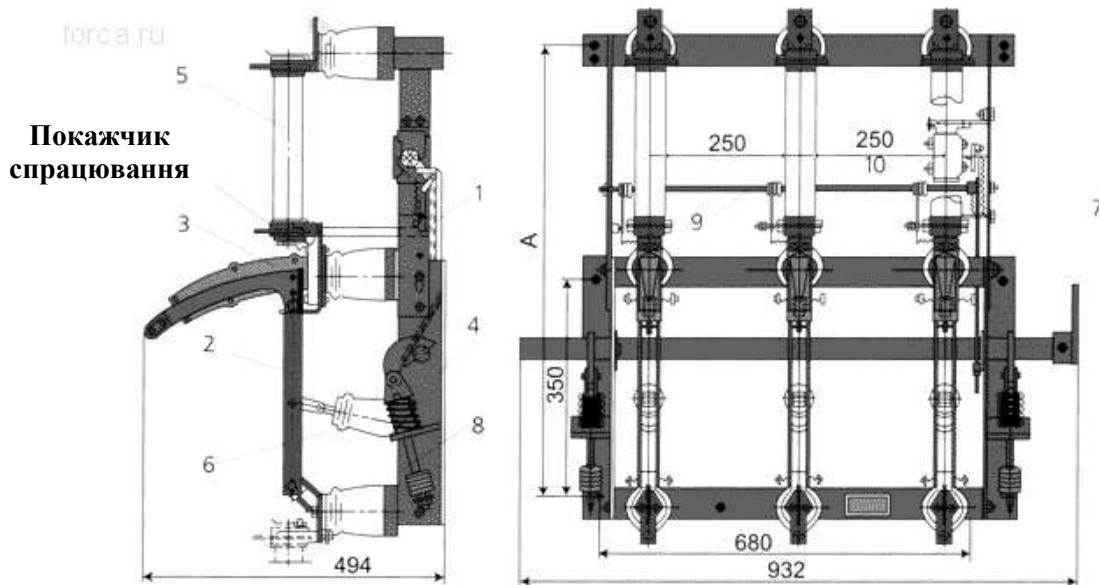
Вимикач навантаження ВНП – 17 з верхнім розміщенням запобіжників: 1 - опорний ізолятор; 2 - ніж; 3 - дугогасильний пристрій, 4 - порцелянова тяга; 5 - патрон запобіжника; 6 - вимикаюча пружина, 7 - важіль для приєднання до приводу, 8 - опорна рама вимикача навантаження; 9 - пристрій, що вимикає вимикач при перегорянні запобіжника на кожному із трьох полюсів; 10 – вимикаючий електромагніт.
